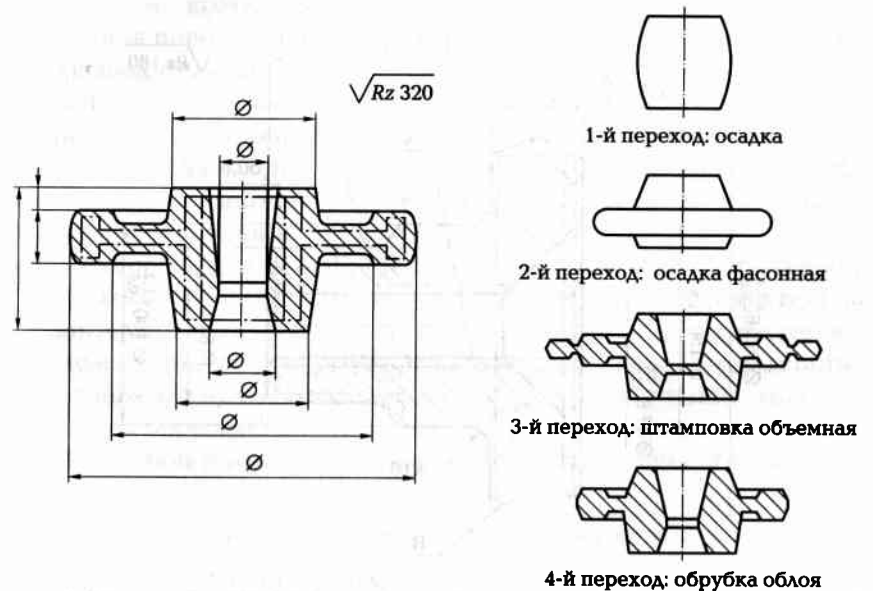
Заготовка — штамповка и последовательность ее изготовления
